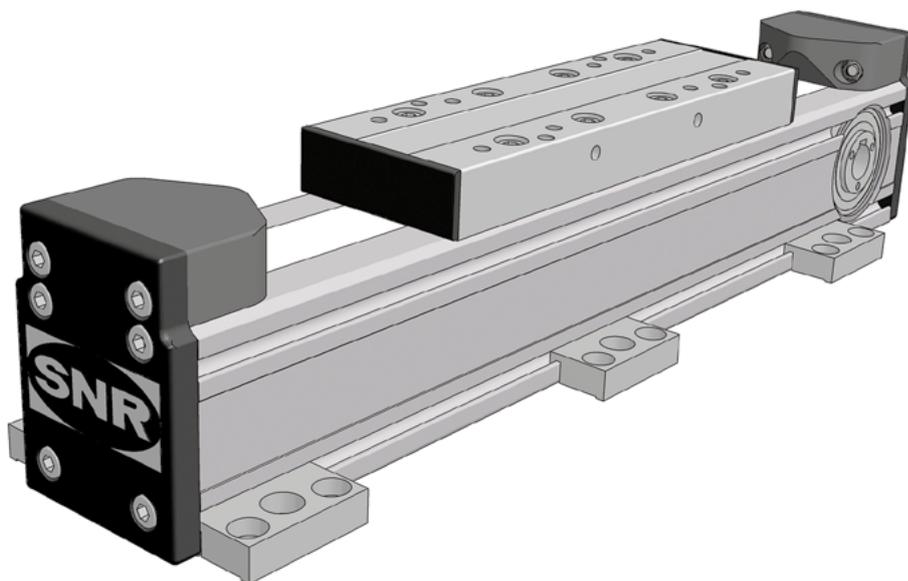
Linearachse AXC mit Befestigungsleisten
